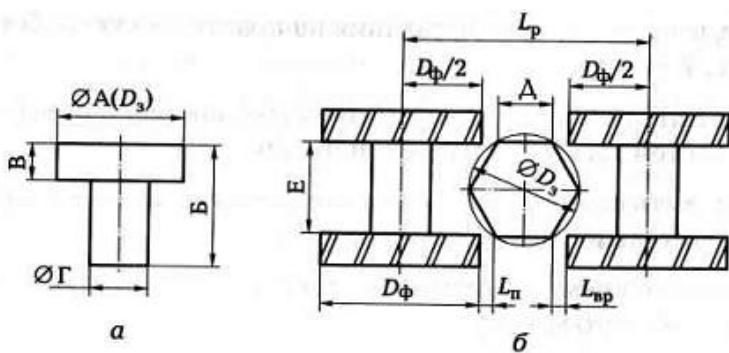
Фрезерование поверхностей: а – заготовка; б – схема обработки
